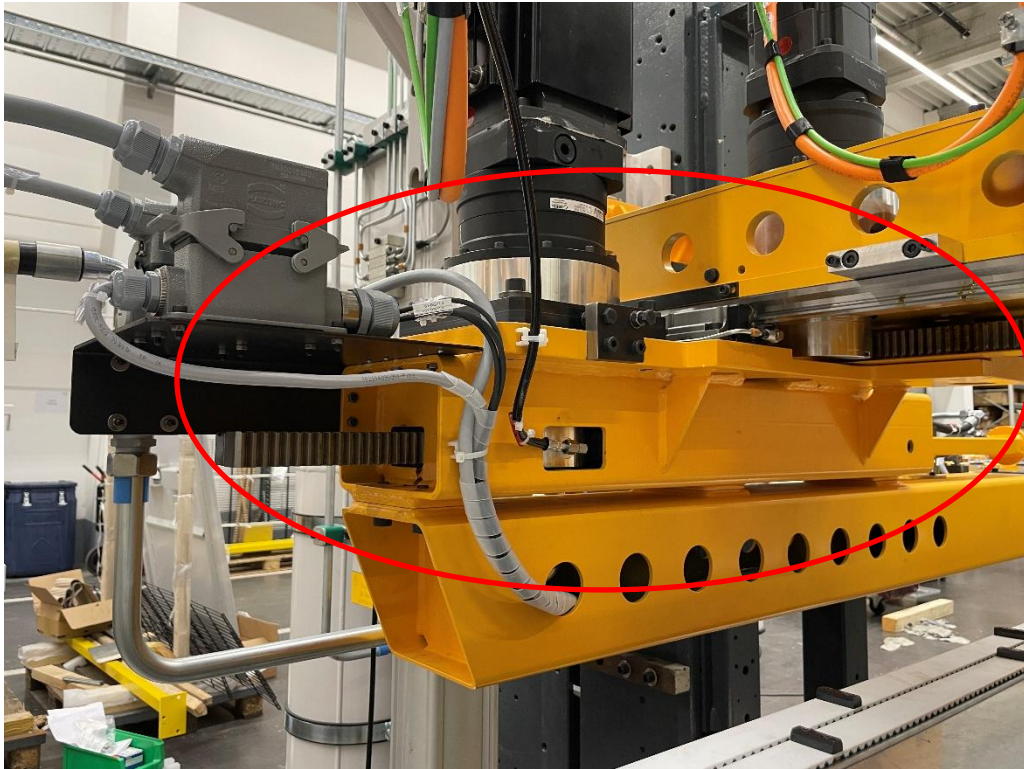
Eingebaute konventionelle Schweißbaugruppe
